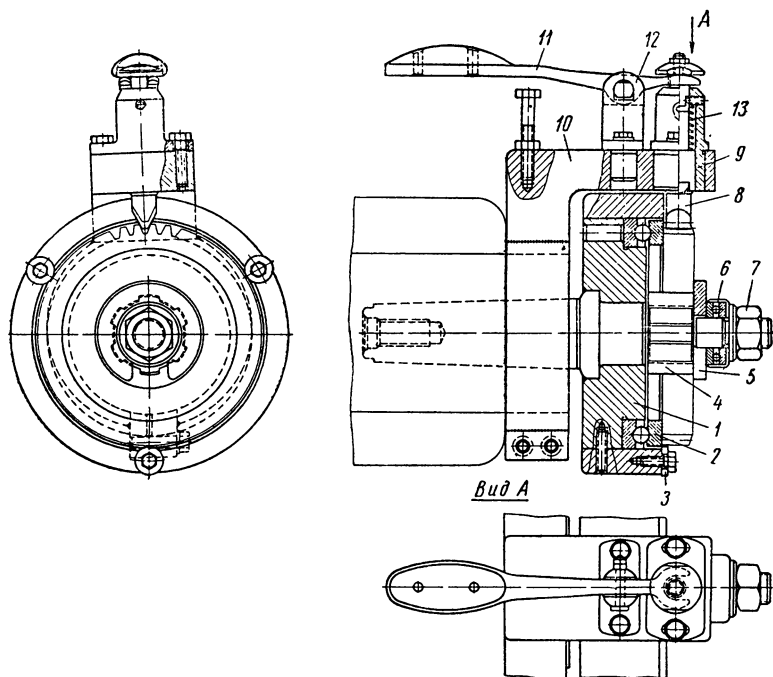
Конструкция шпинделя фрезерной головки для зубозакругления к токарно-копировальному станку.
